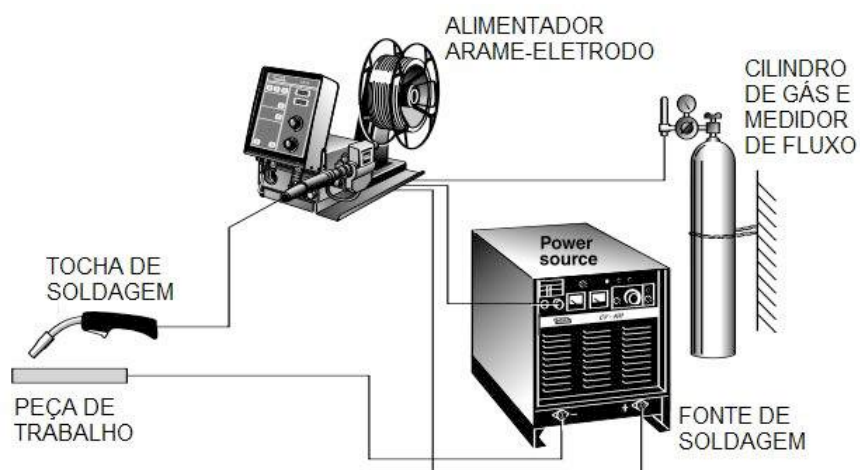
Circuito de soldagem GMAW (ADAPTADO DE LINCOLN ELECTRIC, 2015a)
